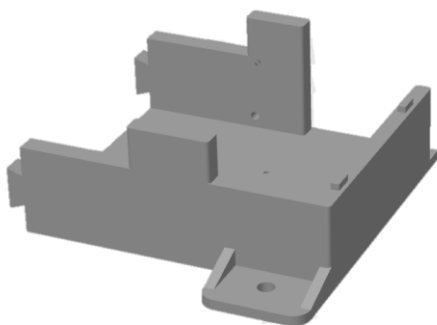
Zobrazení uložení s řídicí jednotkou.
